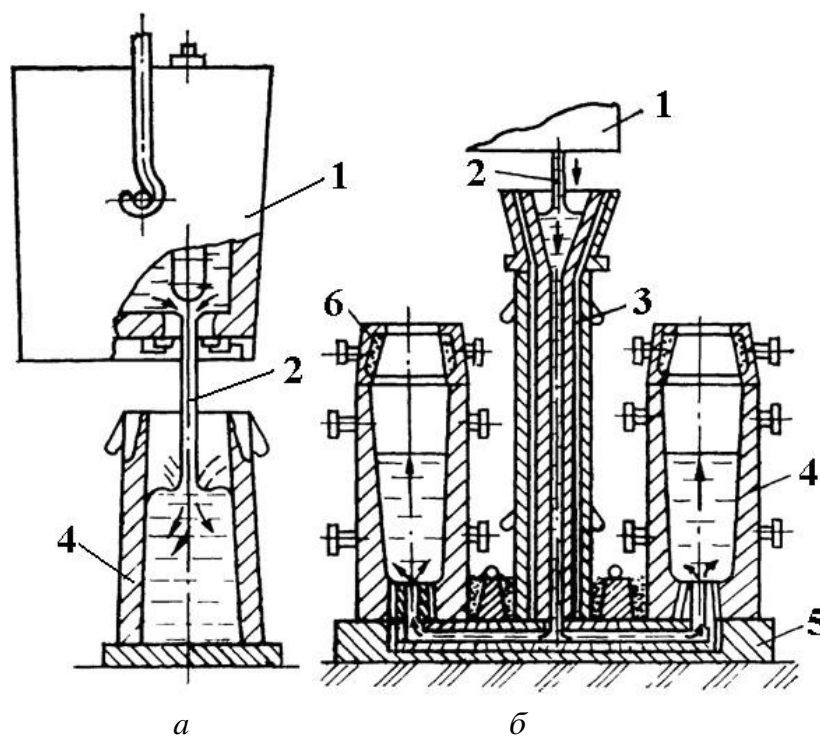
Разливка стали в изложницы: *а* – сверху; *б* – сифоном: 1 – ковш; 2- металл; 3 – центровой литник; 4 – изложницы; 5 – поддон; 6 – надставка для утепления прибыли
